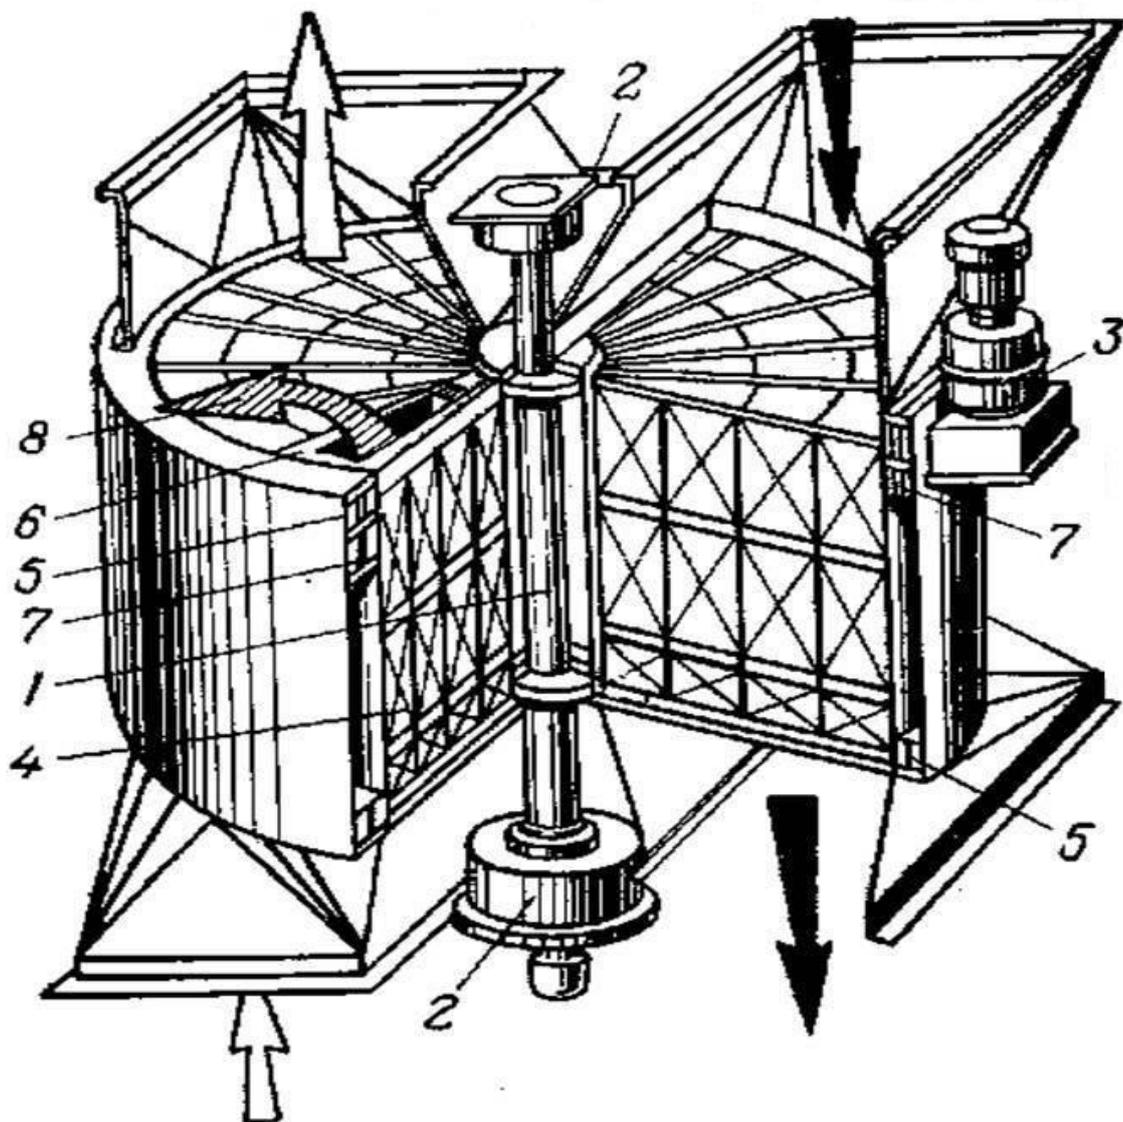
Регенеративный воздухоподогреватель: 1 — вал ротора; 2— подшипники; 3— электродвигатель; 4 — набивка; 5 — наружный кожух; 6 и 7 — радиальное и периферийное уплотнение; 8 — утечка воздуха.
